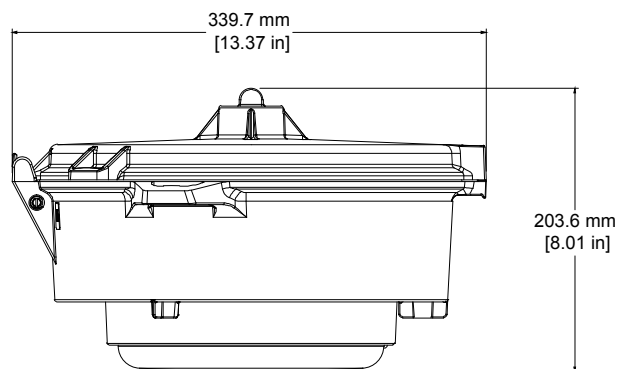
LUMINAIRE AVEC CAPOT SUSPENDU ÉTANCHE
